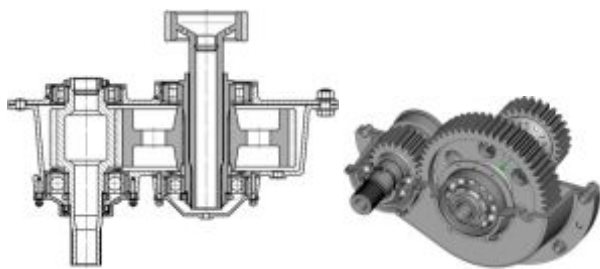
Схема сборки и аксонометрия объёмной модели первой ступени редуктора
